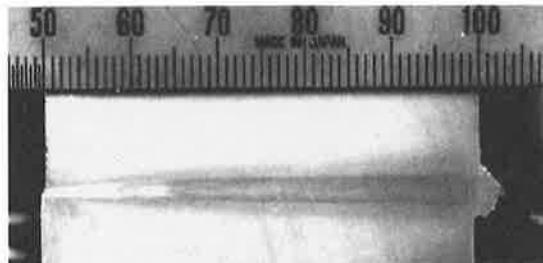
アルミニウム合金の電子ビーム溶接継手例
